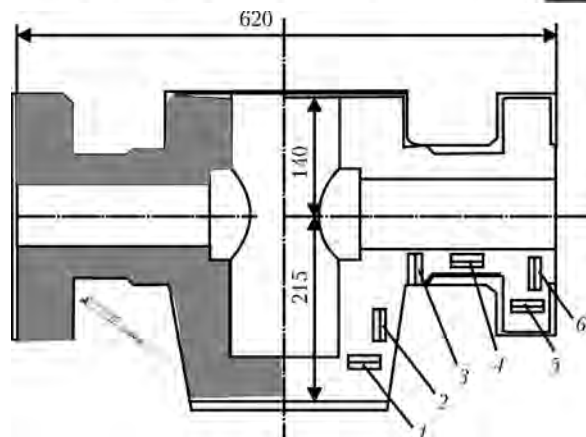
Макроструктура (ЭШЛ) корпуса фланцевой задвижки и схема вырезки образцов для оценки анизотропии ее механических свойств; 1-6 — номера образцов (см. табл. 2)
